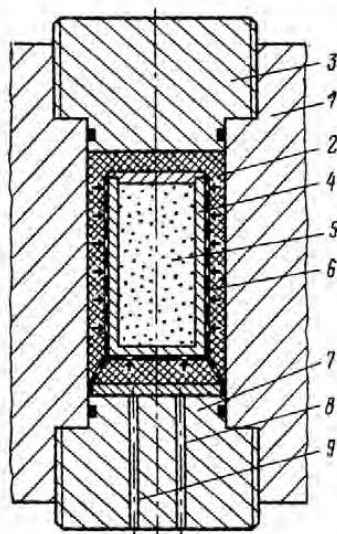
Принципиальная схема изостатического прессования: 1 – сосуд высокого давления; 2 – жидкость высокого давления; 3 – верхний затвор; 4 – упругая форма; 5 – прессуемый порошок; 6 – перфорированная корзина; 7 – нижний затвор; 8 – подвод высокого давления; 9 – отвод жидкости.
